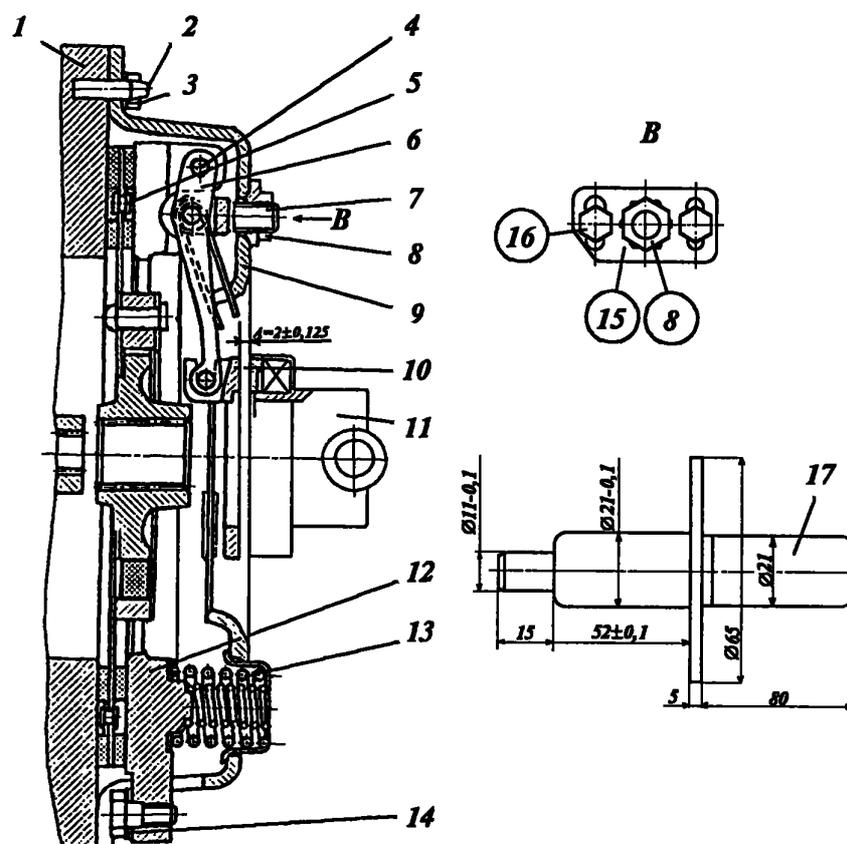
Муфта сцепления: 1 - маховик двигателя; 2 - установочный штифт; 3, 16 - болты; 4 - палец; 5 - ведомый диск; 6 - отжимной рычаг; 7 - вилка; 8 - гайка регулировочная; 9 - опорный диск; 10 - опора; 11 - отводка; 12 - нажимной диск; 13 - нажимные пружины; 14 - пластины; 15 - стопорная пластина; 17 - оправка
